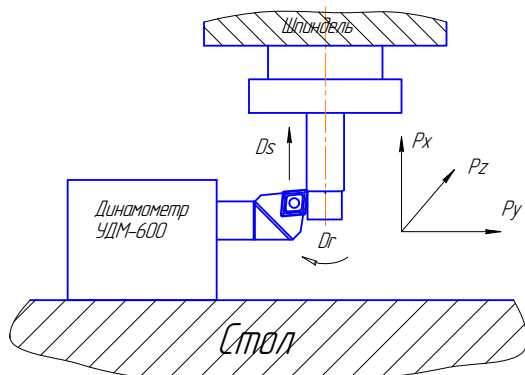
Схема измерения силы резания на фрезерном станке
